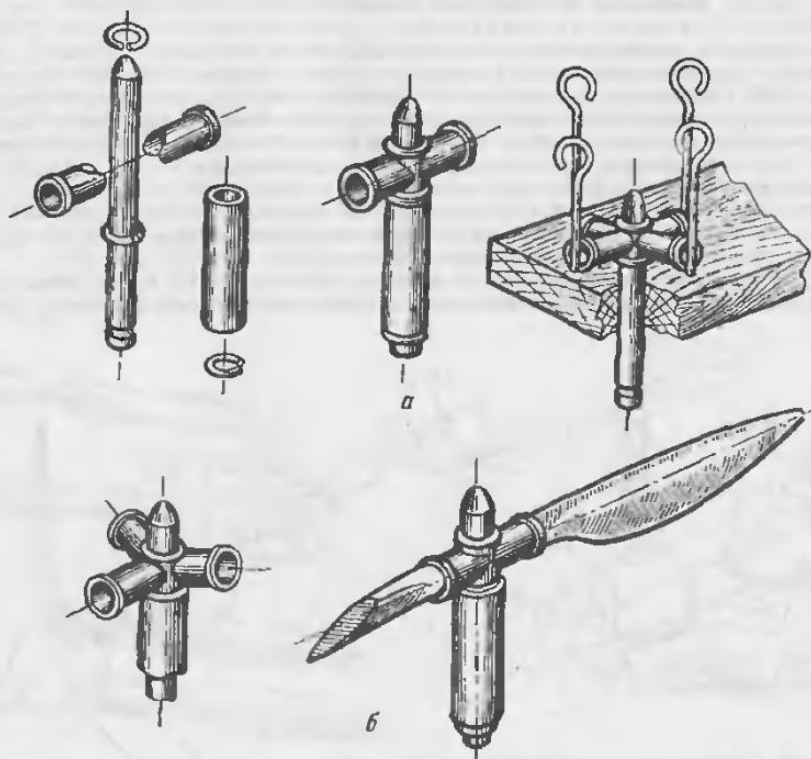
Пример изготовления втулок винтов пайкой: а - подборка втулки перед пайкой; б - втулка в сборе
